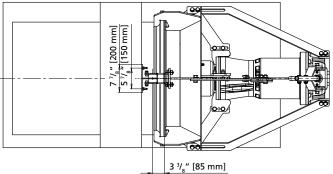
Dimensiones de Amaline 500, 600, 800 - material de la carcasa del motor: fundición gris
